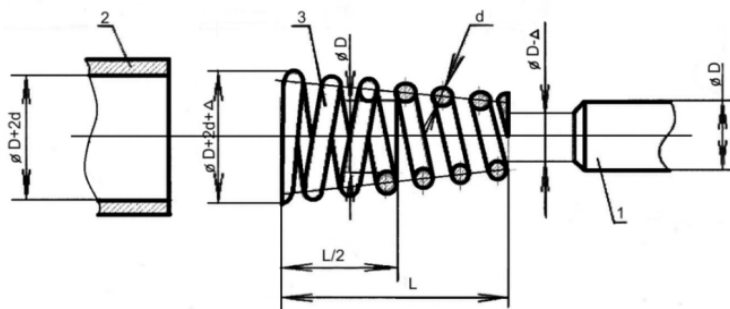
Конический подшипник скольжения для возвратно-вращательного движения
